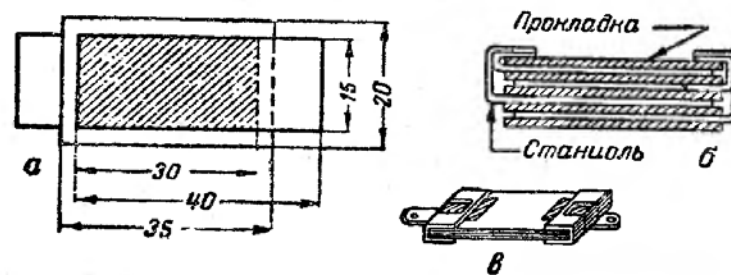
Устройство постоянного конденсатора: а — размеры пластин и прокладок; б — способ укладки пластин; в — готовый конденсатор.
